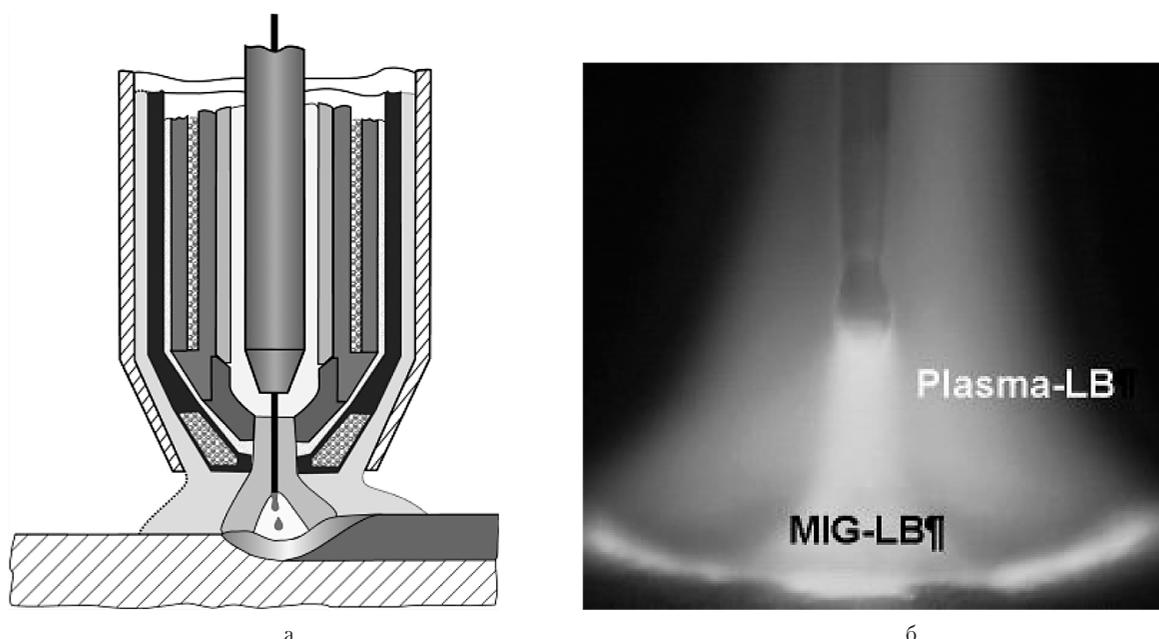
Схема процесса (а) и фото сжатой дуги и дуги плавящегося электрода (б) гибридной плазменной сварки плавящимся электродом
